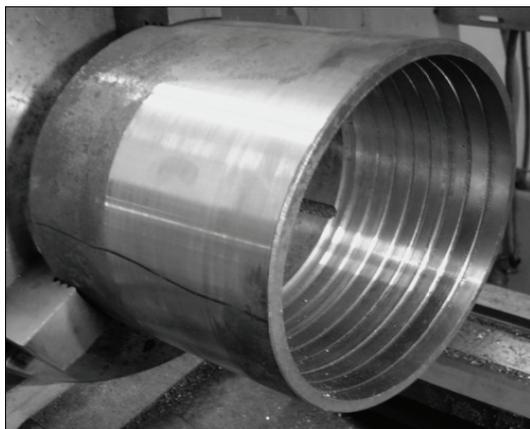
Обрабатываемая заготовка, зажатая в патроне станка
